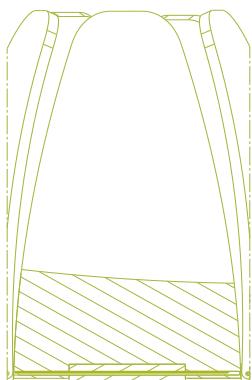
Vista de detalle del ensamblaje del enganche inferior mediante un pasador
